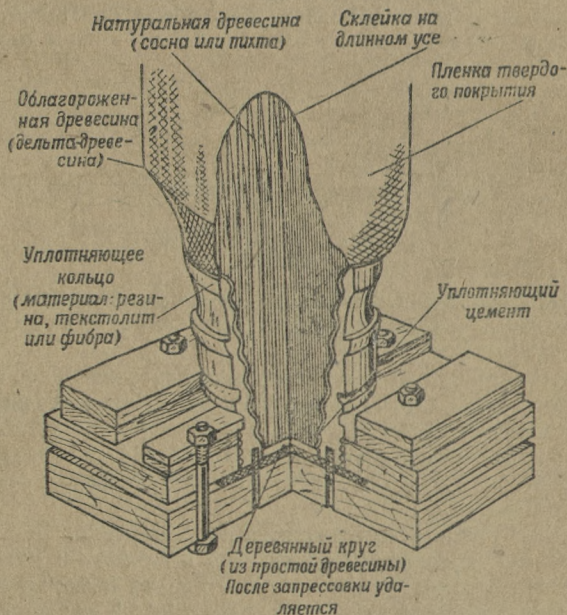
Разрез крепления деревянной лопасти в стакане и приспособления для заливки зазоров резьбы цементом
